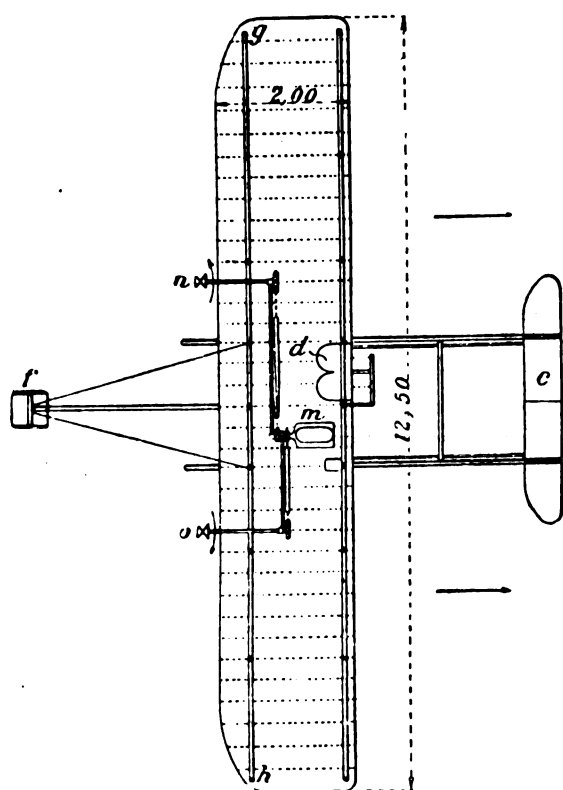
e 8. — Biplano Wright - Pianta, elevazione e vista.
